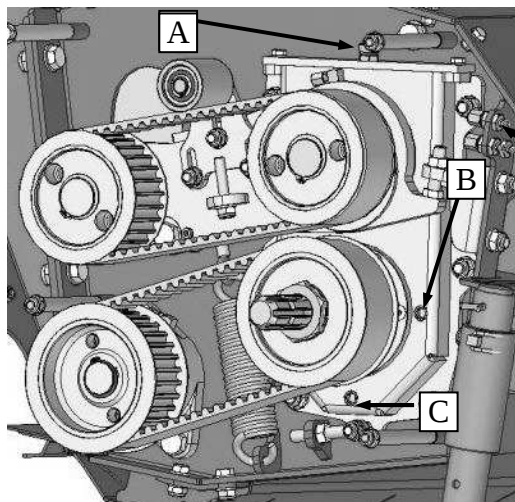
Точки контроля и замены масла зубчатой передачи плющилки
